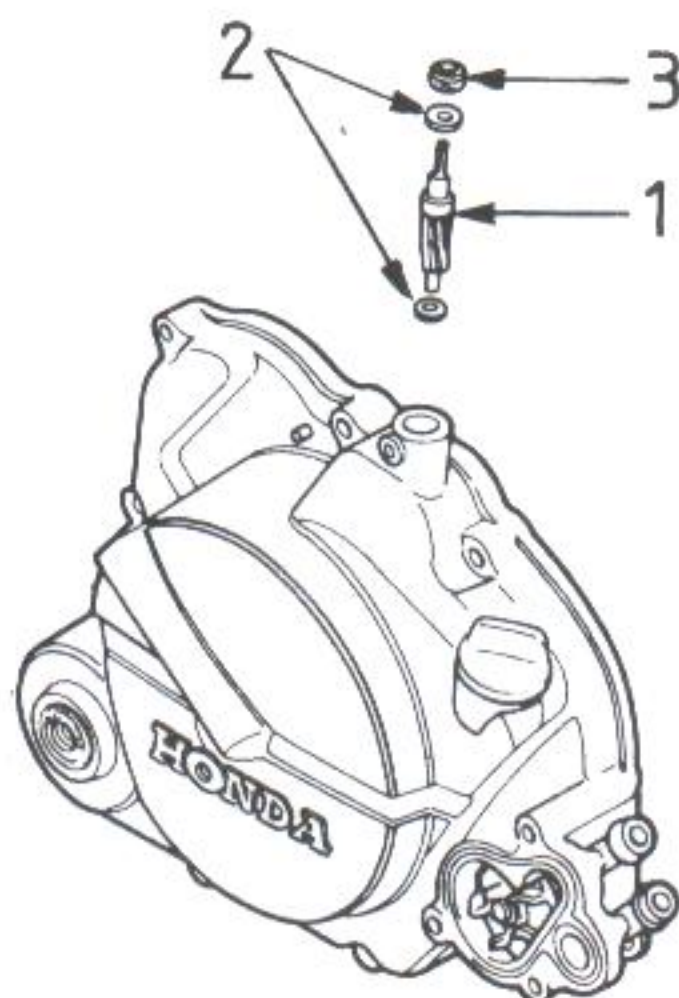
Toma de movimiento del cuentarrevoluciones de la figura anterior. 1, engranaje que se ajusta al tornillo sinfín; 2, arandelas; 3, pequeño retén de grasa.
